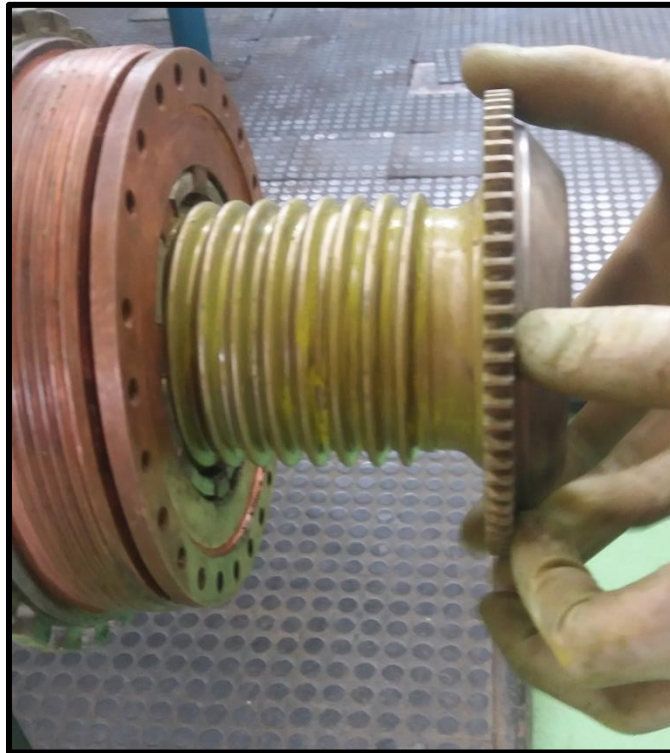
Montaje del Race botton en la Blade and bushes assembly
